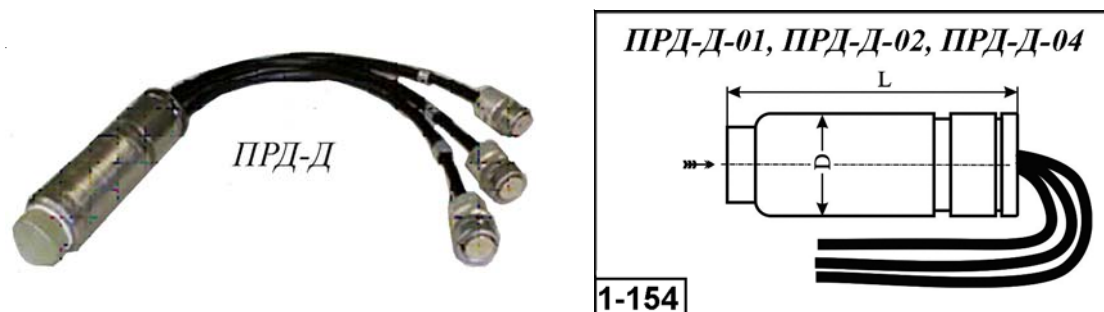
Внешний вид и габаритные размеры детектора серии ПРД-Д.
